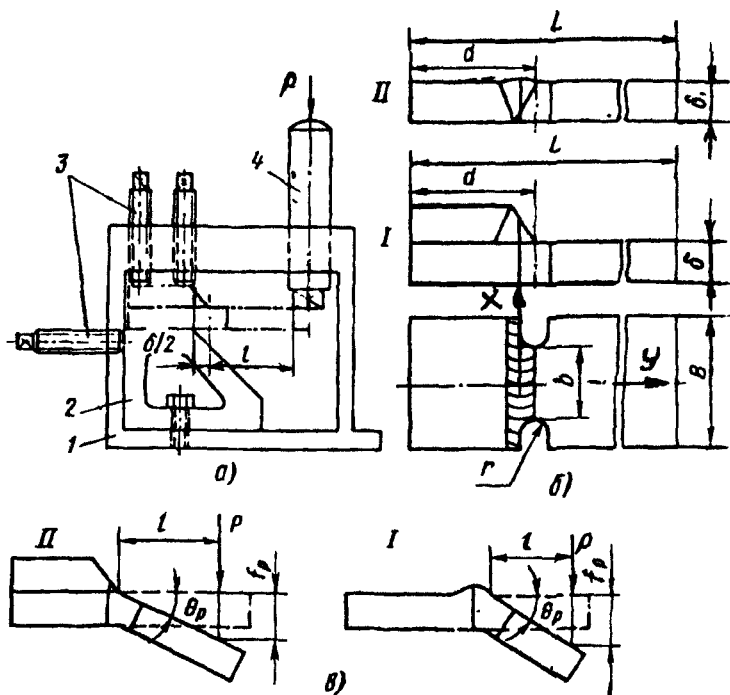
Схема испытания (а) сварного соединения для определения угла изгиба: 1 — корпус; 2 — опора; 3 — упорные болты; 4 — шток. Типы образцов (б); I — с угловым швом; II — со стыковым швом. Вид образцов после испытания (в).
